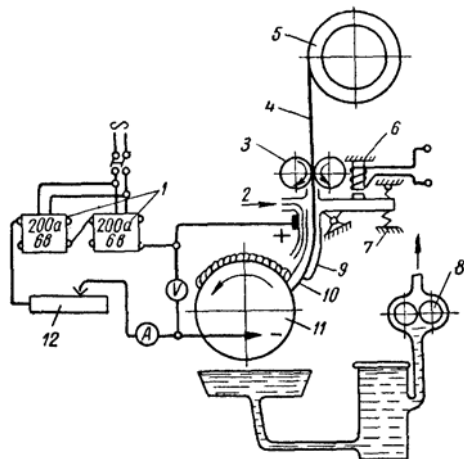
Принципиальная схема установки для вибродуговой наплавки
